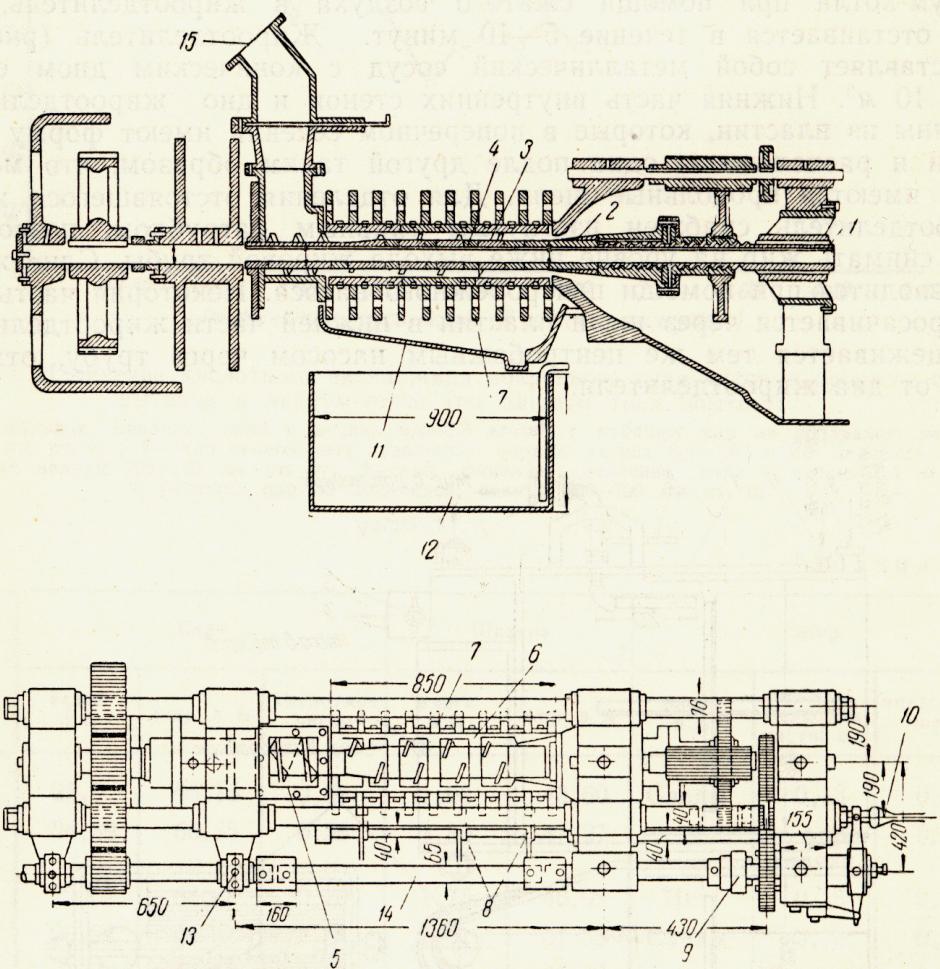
Схема устройства зеерного пресса для отжимания шквары:
